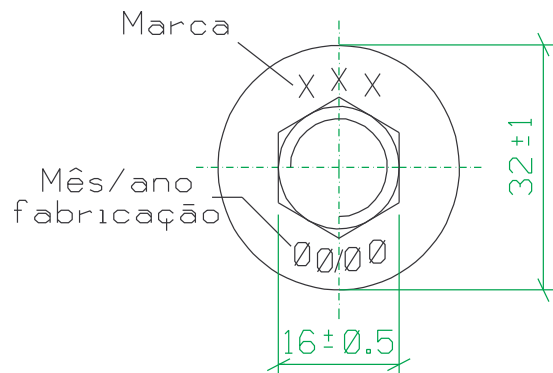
FIGURA - PINO AUTOTRAVANTE PARA ISOLADOR PILAR
